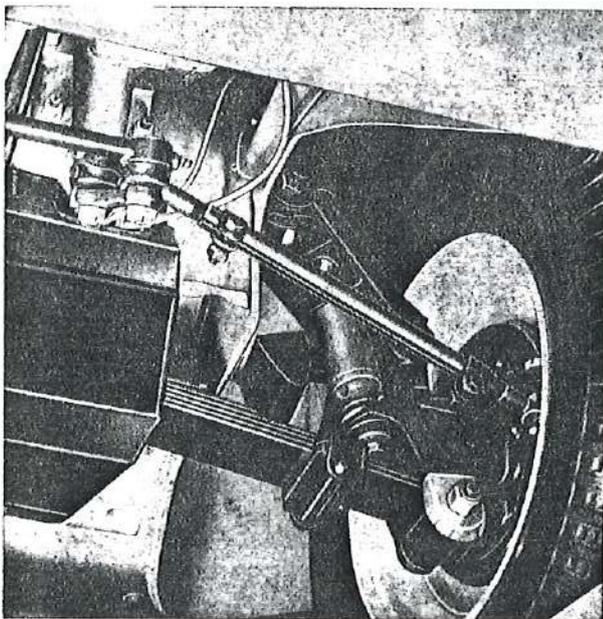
Detalle de la suspensión anterior, lado izquierdo del coche.
